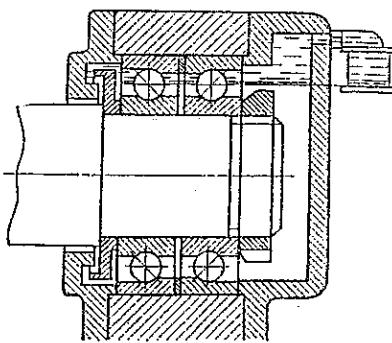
Сливное отверстие в крышки корпуса тихоходного подшипника
